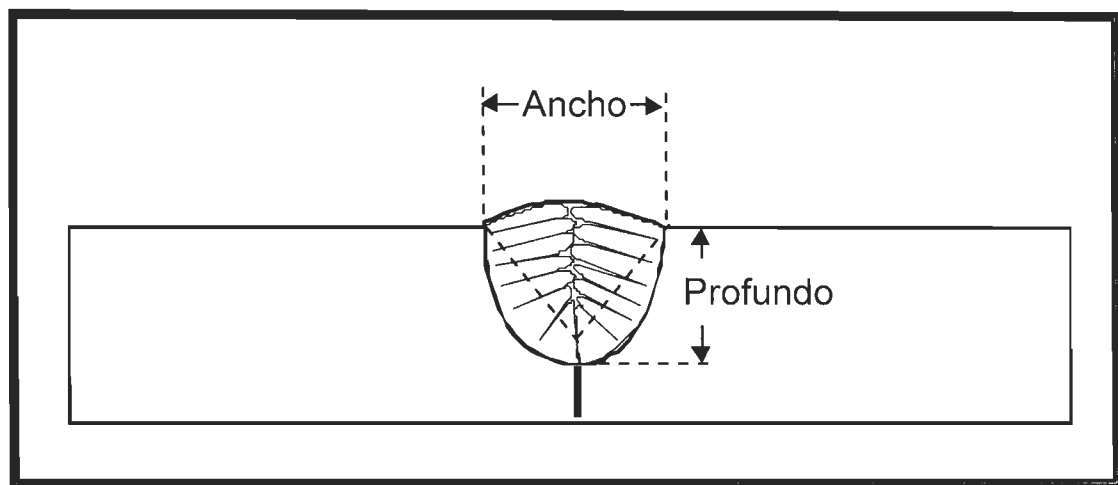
Agrietamiento inducido en la forma del cordón de soldadura [11].
